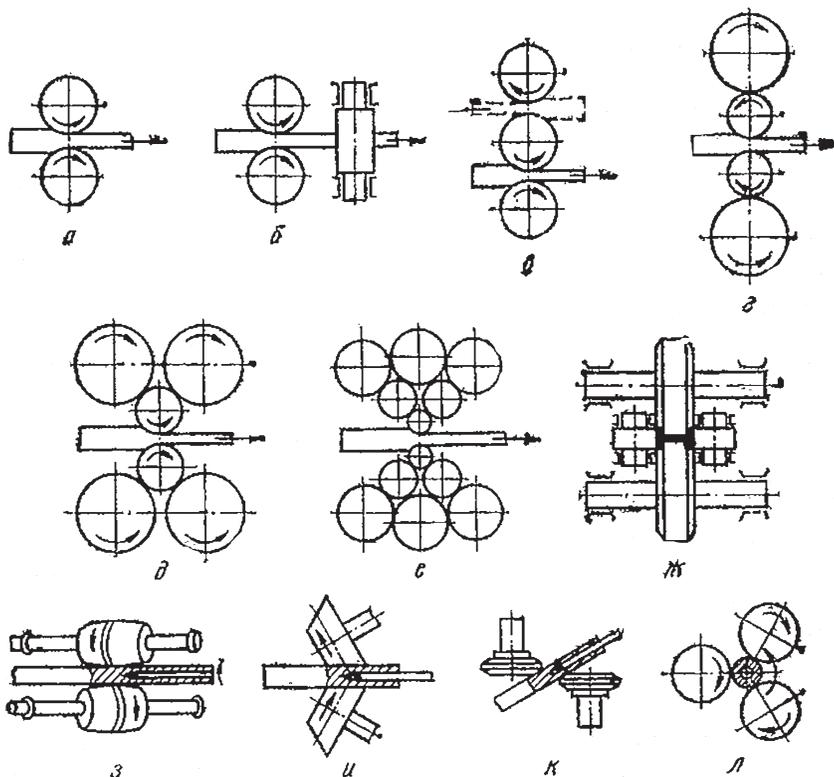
Классификация прокатных станов по конструкции и расположению валков: а – дуо; б – с горизонтальной и вертикальной парой валков; в – трио; г – кварто; д – шестивалковые; е – двенадцати двадцативалковые; ж – универсальные балочные; з-к – трубoproкатные прошивные станы для прошивки отверстий в сплошных заготовках или слитках круглого сечения; л – трубoproкатные прошивные станы для удлинения прошитых трубных заготовок
